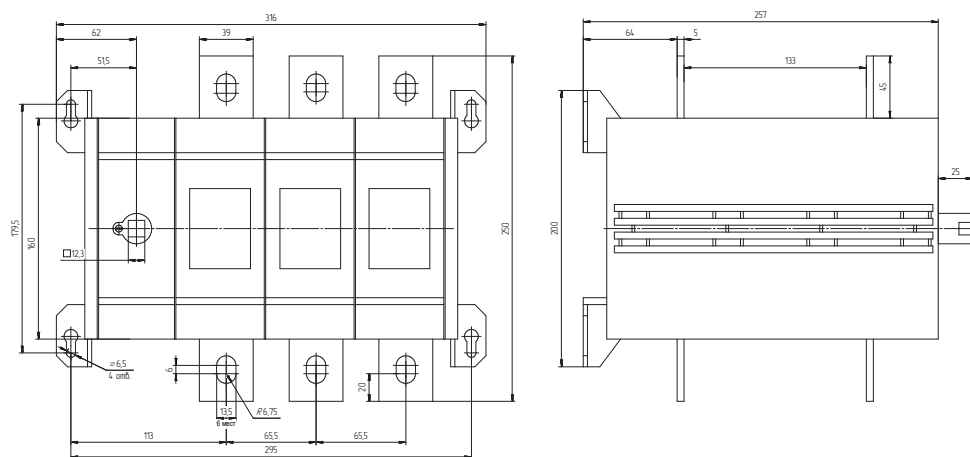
Выключатель-разъединитель 630 – 800 А реверсивного исполнения
